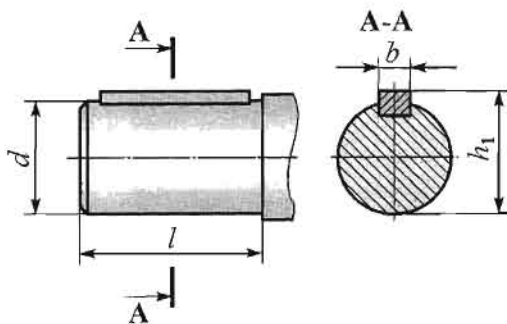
Размеры конца тихоходного вала мотор-редуктора
